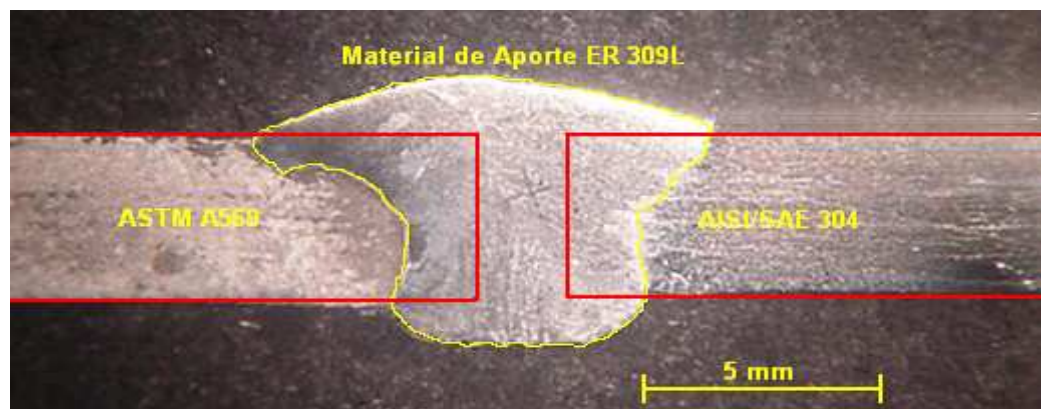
Macrografía de la junta disímil AISI/SAE 304 y ASTM A569 soldado con un electrodo ER309L.
